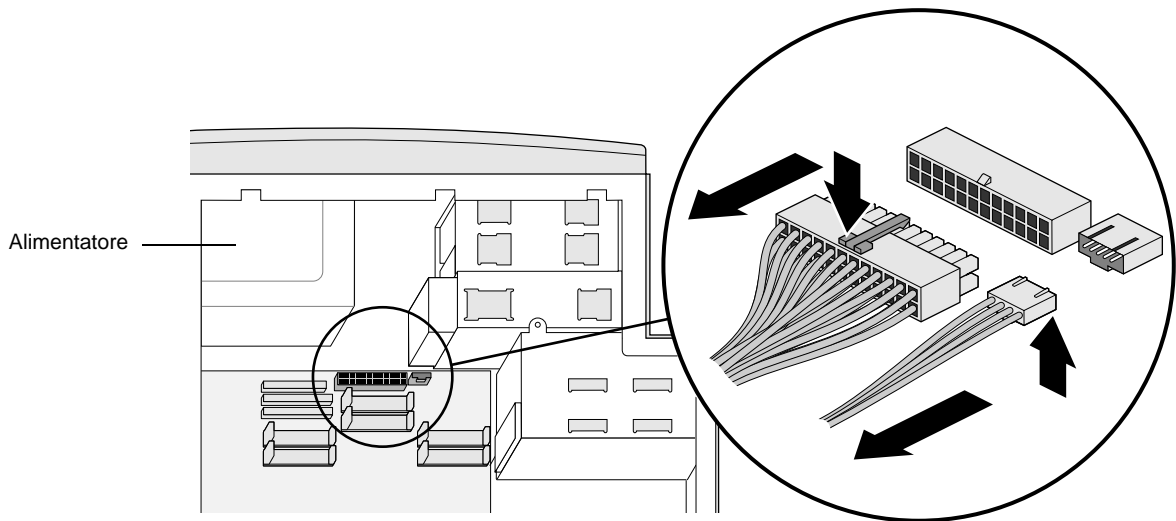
Scollegamento dei cavi di alimentazione dalla scheda di sistema
